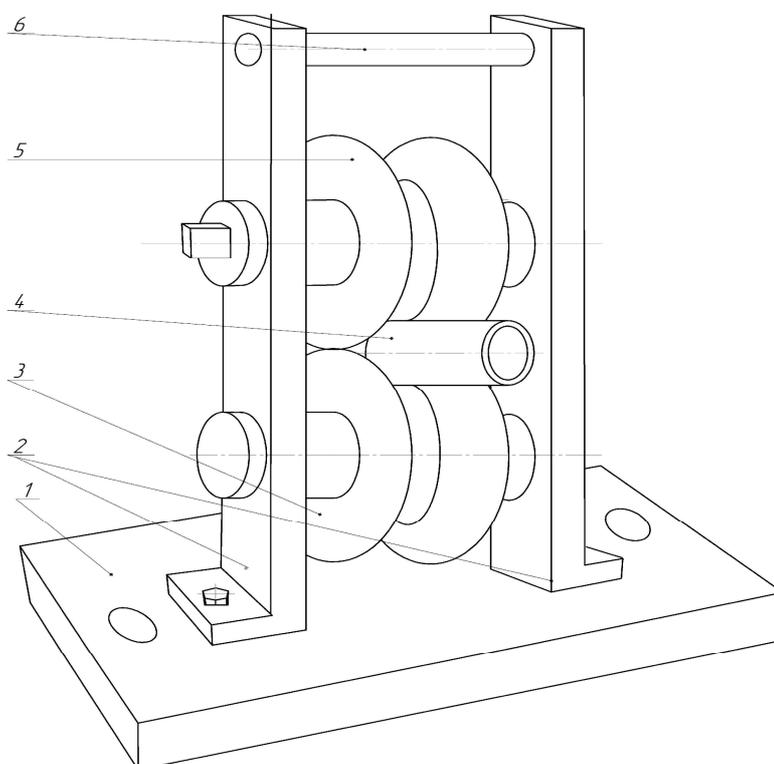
Общий вид установки для обжатия втулок вращающимися матрицами: 1 – стальная платформа основа, 2- вертикальные стойки, 3 – нижний ролик, 4 – восстанавливаемая втулка, 5 – верхний ролик, 6 – упорная планка
